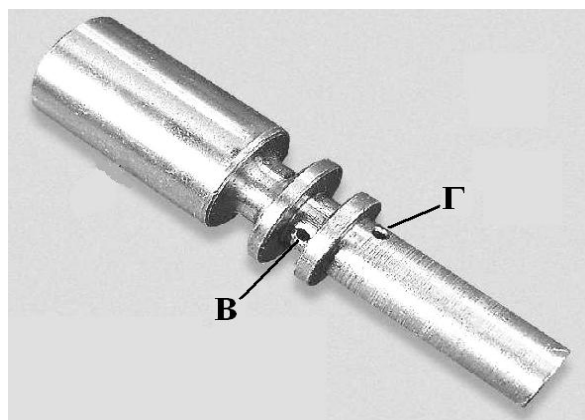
Общий вид поршня главного цилиндра гидропривода выключения сцепления автомобилей ВАЗ
